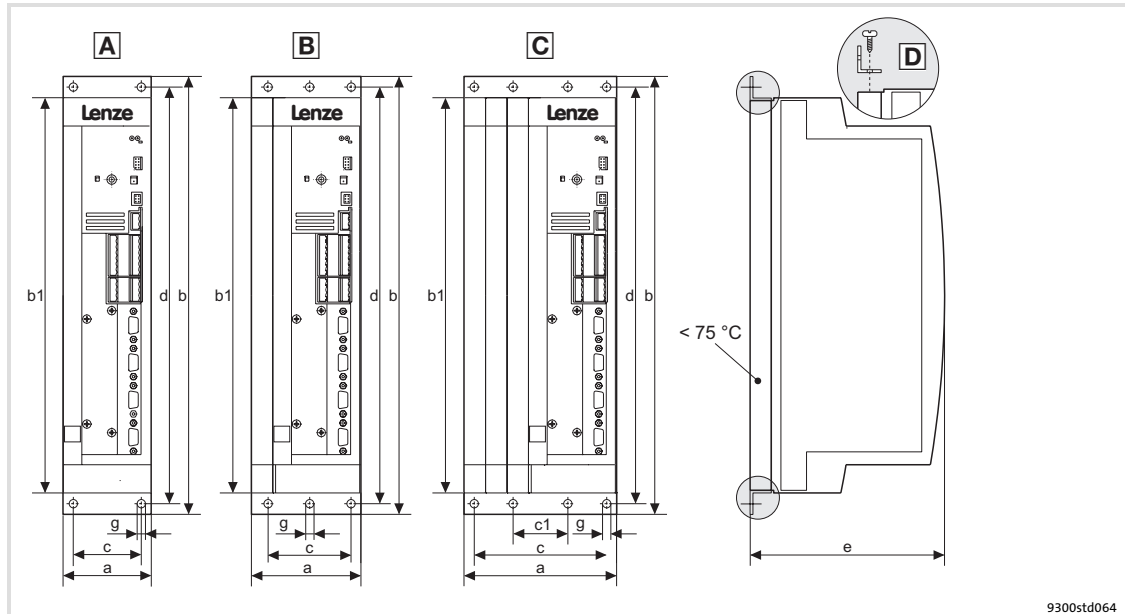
Abmessungen Montage in "Cold Plate"-Technik 0,37 ... 11 kW
